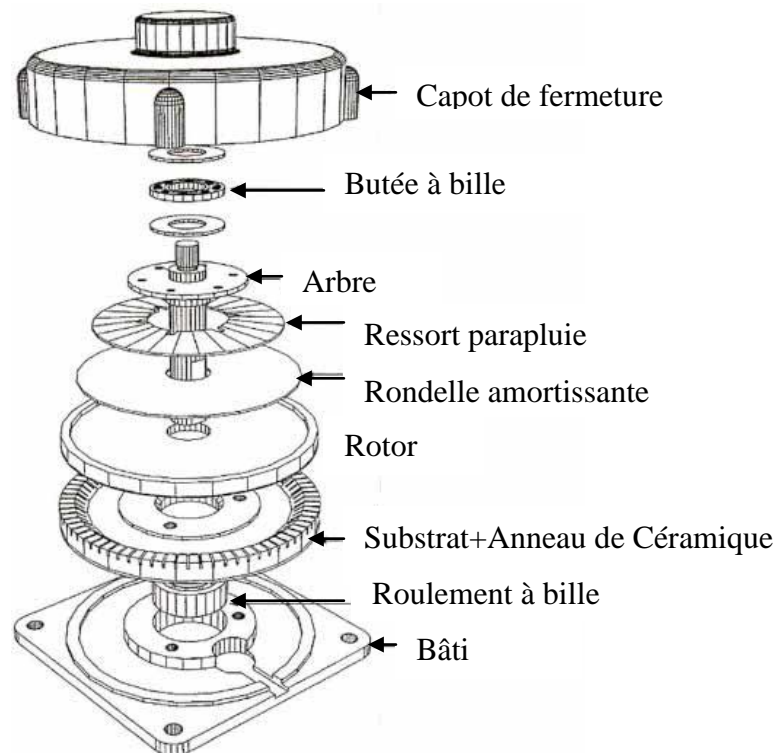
Vue éclatée du moteur SHINSEI USR60 [4].
